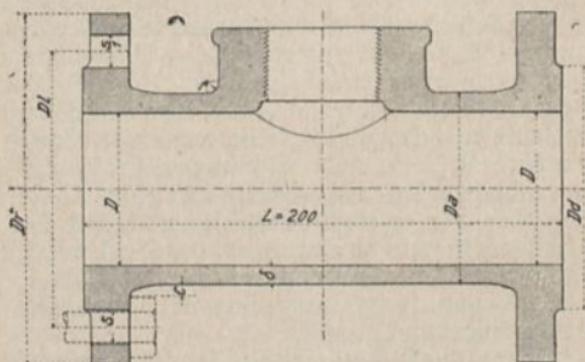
Gußeisernes Gewinde-Abzweigstück.
